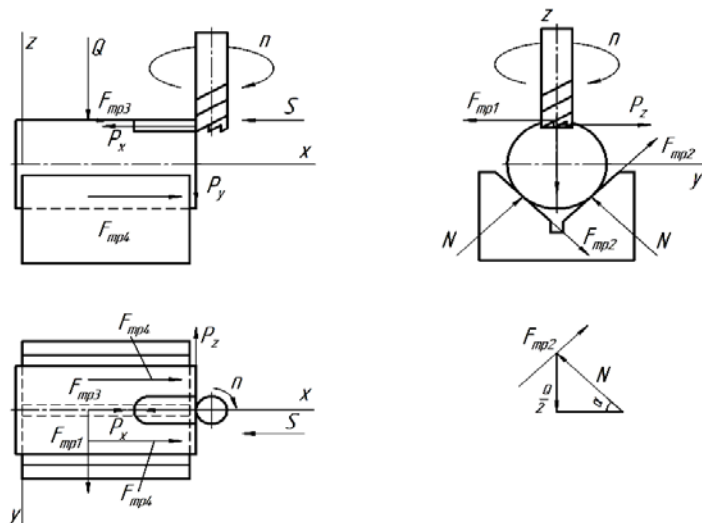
Схема сил діючих на заготовку під час обробки при закріпленні у призмах
